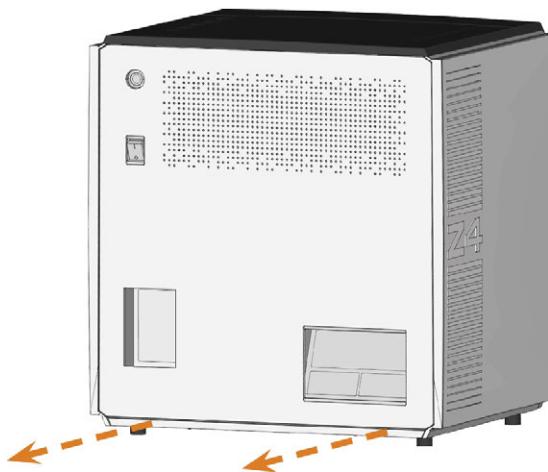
RETIRER LE COUVERCLE DU PANNEAU ARRIÈRE
